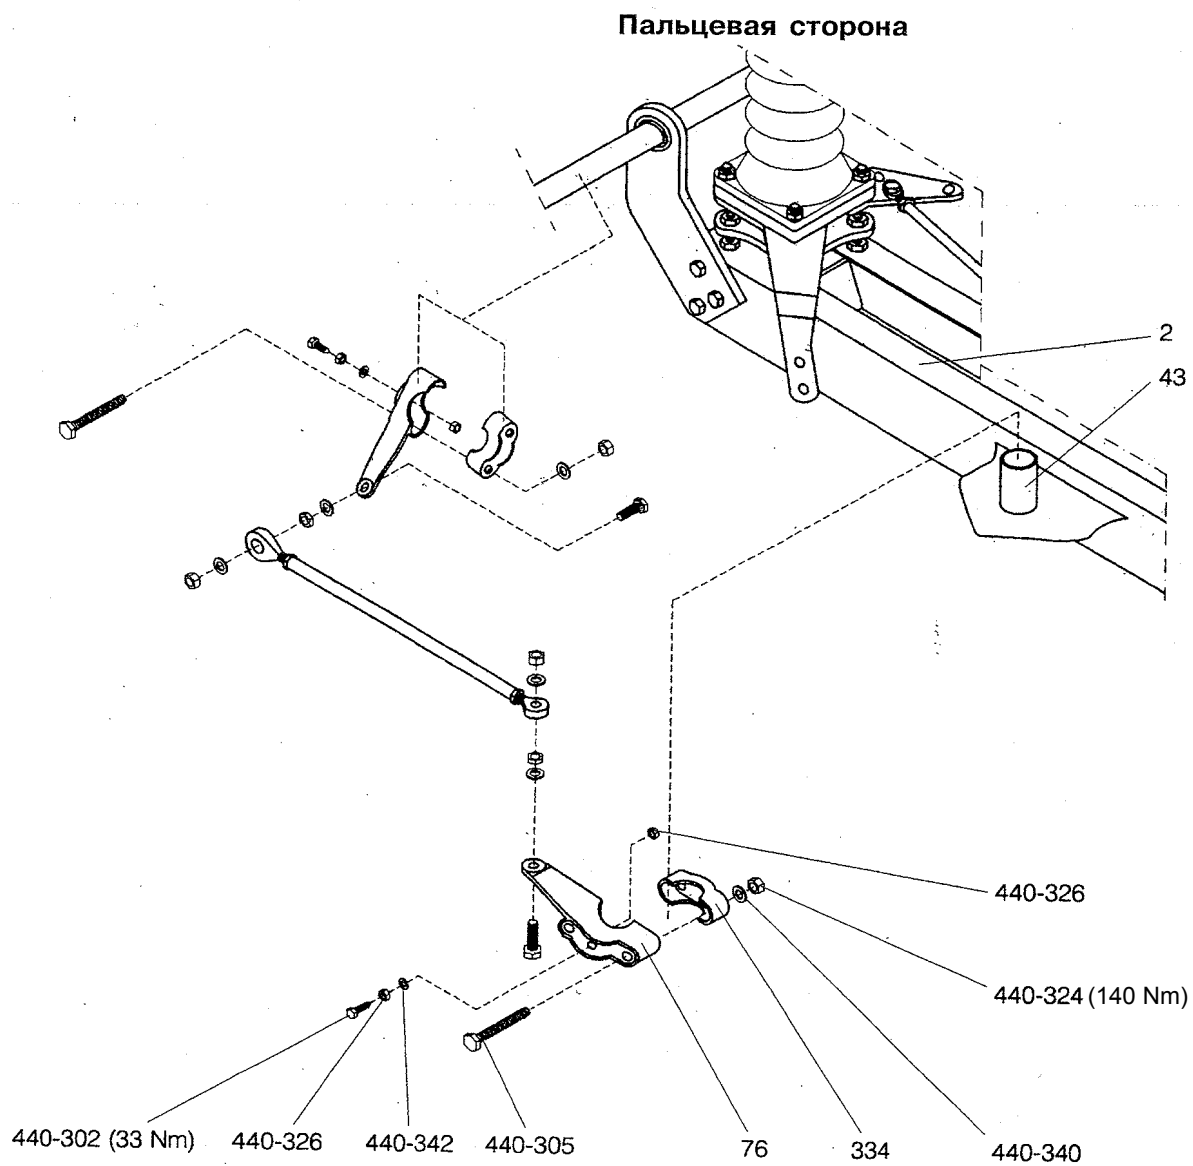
Установка приводного механизма заземлителя, непосредственный и раздельный монтаж. Установка приводного рычага (76) при расположении заземлителя на пальцевой стороне
